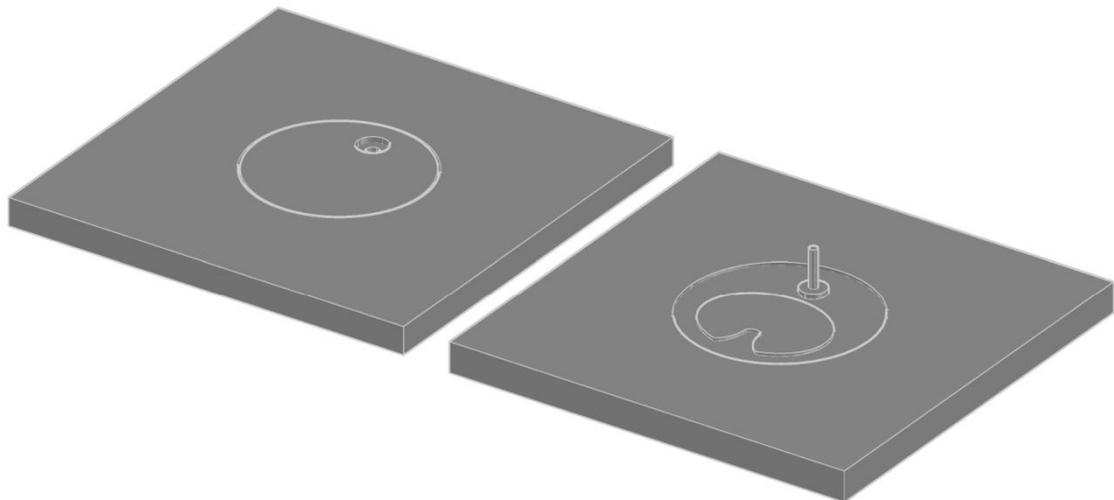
Molde para la pieza 1.2 tapa pequeña. Detalle del fresado.
